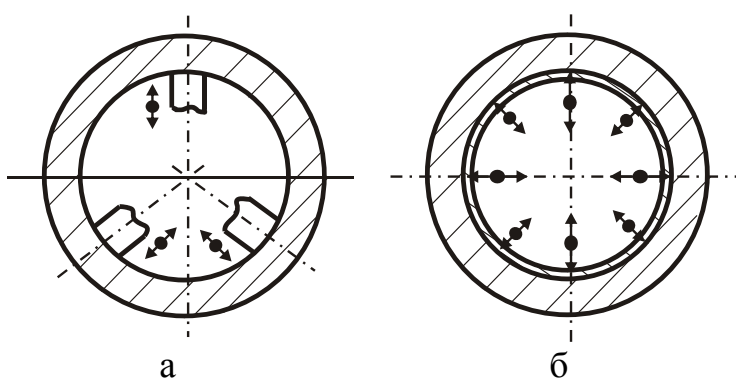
Схема базирования заготовки с главной базой, имеющей вид цилиндрического отверстия, на самоцентрирующее устройство: а - с тремя кулачками; б - с тонкостенной втулкой, разжимаемой гидропластом, роликами и т.д.
